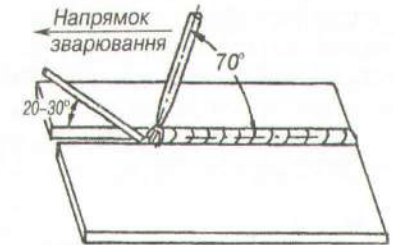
Зварювання тонких листів з подачею присаджувального металу в дугу
